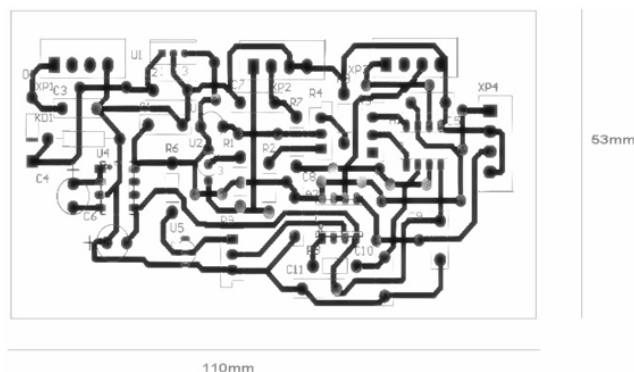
Esquema PCB de la tarjeta acondicionadora.
